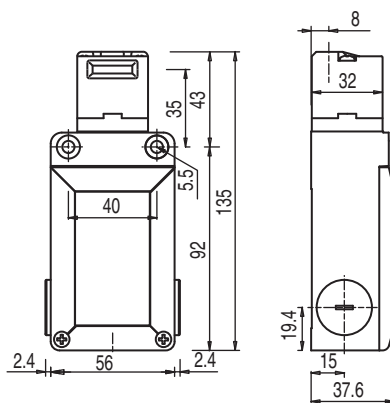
Dimensioni di L100-P3C3-M20-MLM24 in mm
